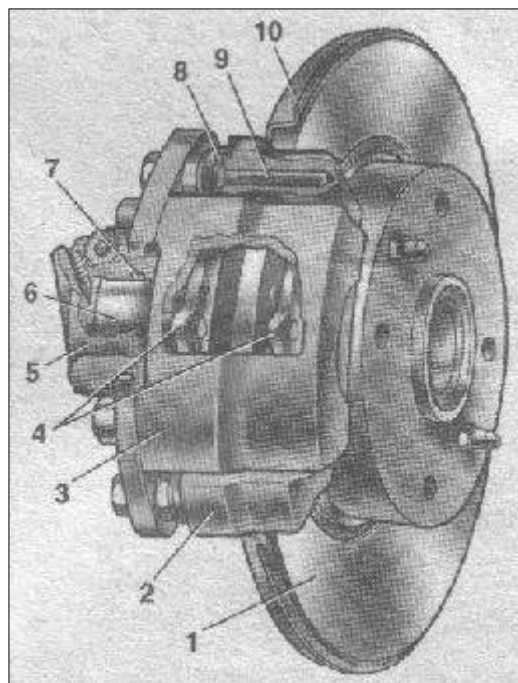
Гальмівний механізм переднього колеса: 1 – гальмовий диск; 2 – напрямна колодок; 3 – супорт; 4 – гальмові колодки; 5 – циліндр; 6 – поршень; 7 – ущільнювальне кільце; 8 – захисний чохол напрямного пальця; 9 – напрямний палець; 10 – захисний кожух.
